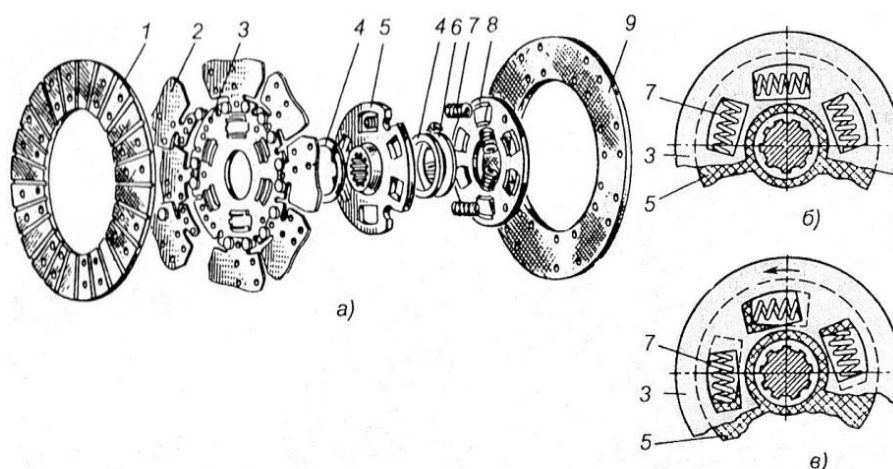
Ведомый диск: а – детали; б – нерабочее положение гасителя крутильных колебаний; в – рабочее положение гасителя; 1,9 – фрикционные накладки диска; 2 – пластинчатая пружина; 3 – диск; 4 – кольца; 5 – ступица; 6 – регулировочная шайба; 7 – пружина; 8 – диск гасителя
